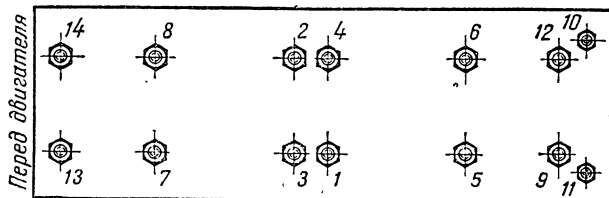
Схема затяжки гаек шпилек коренных подшипников.
